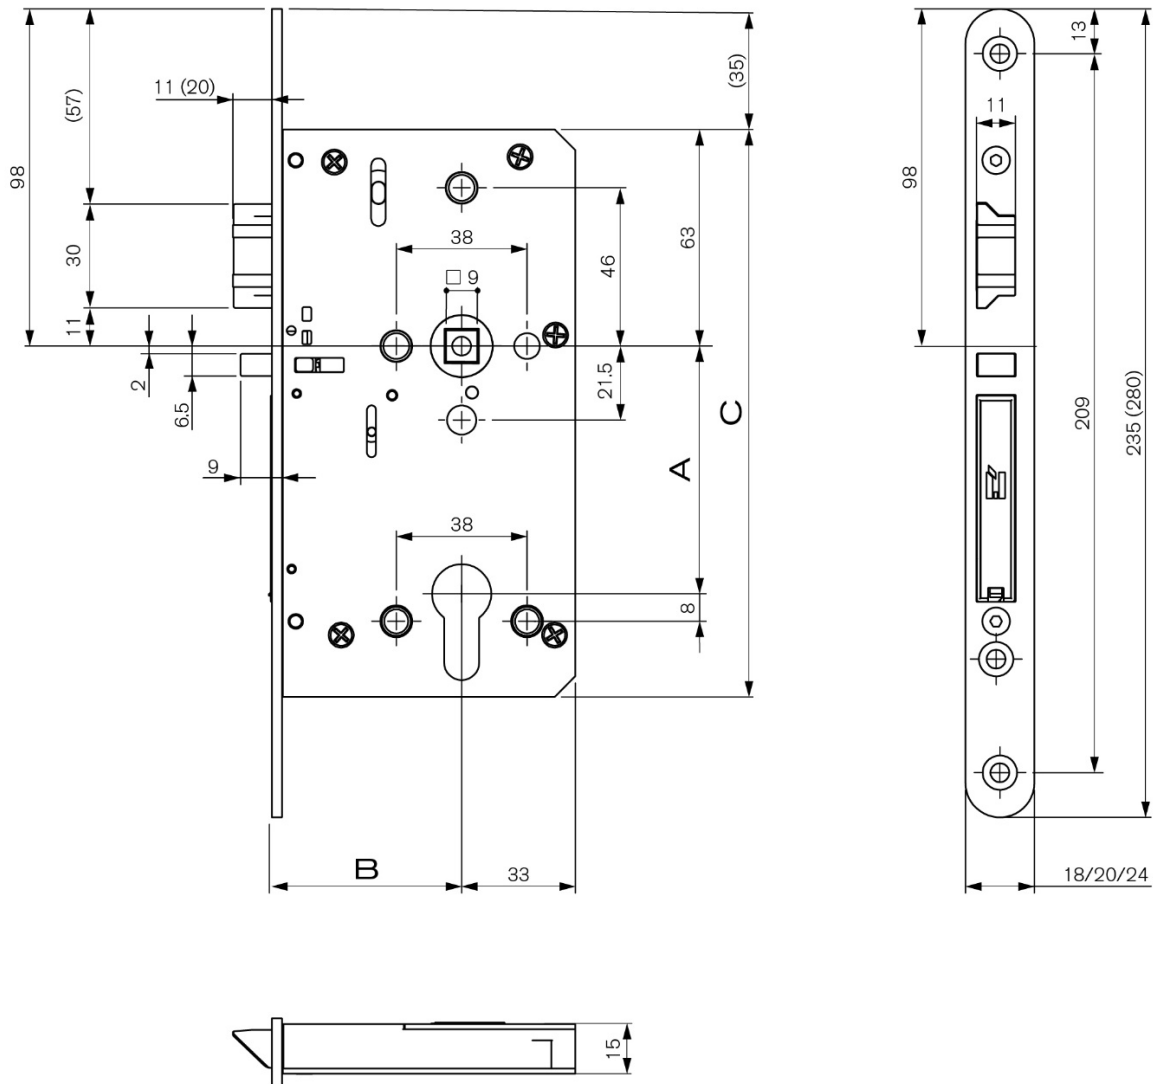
Abmessungen für Schlossinstallation – Profilzylinder 72 / Rundzylinder 74
